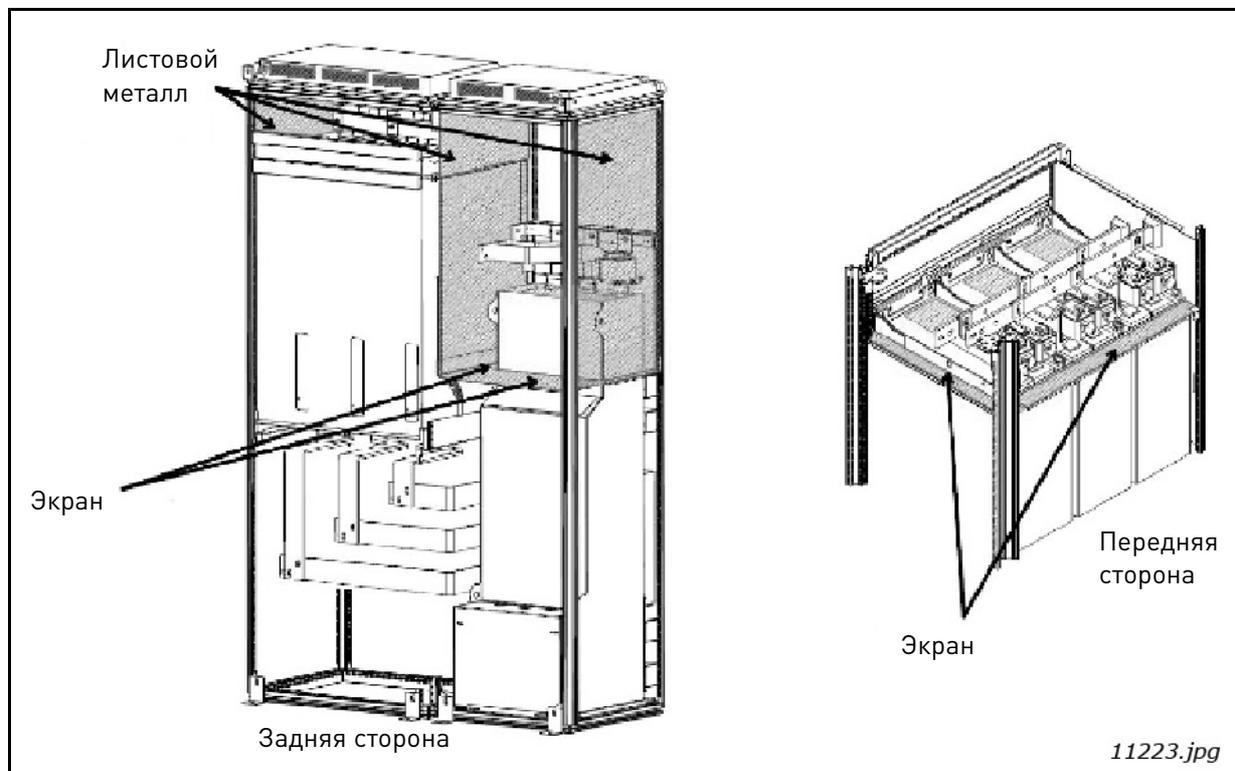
Направляющие охлаждающего воздуха в шкафах для устройства AFE и фильтра LCL типоразмера FI13
